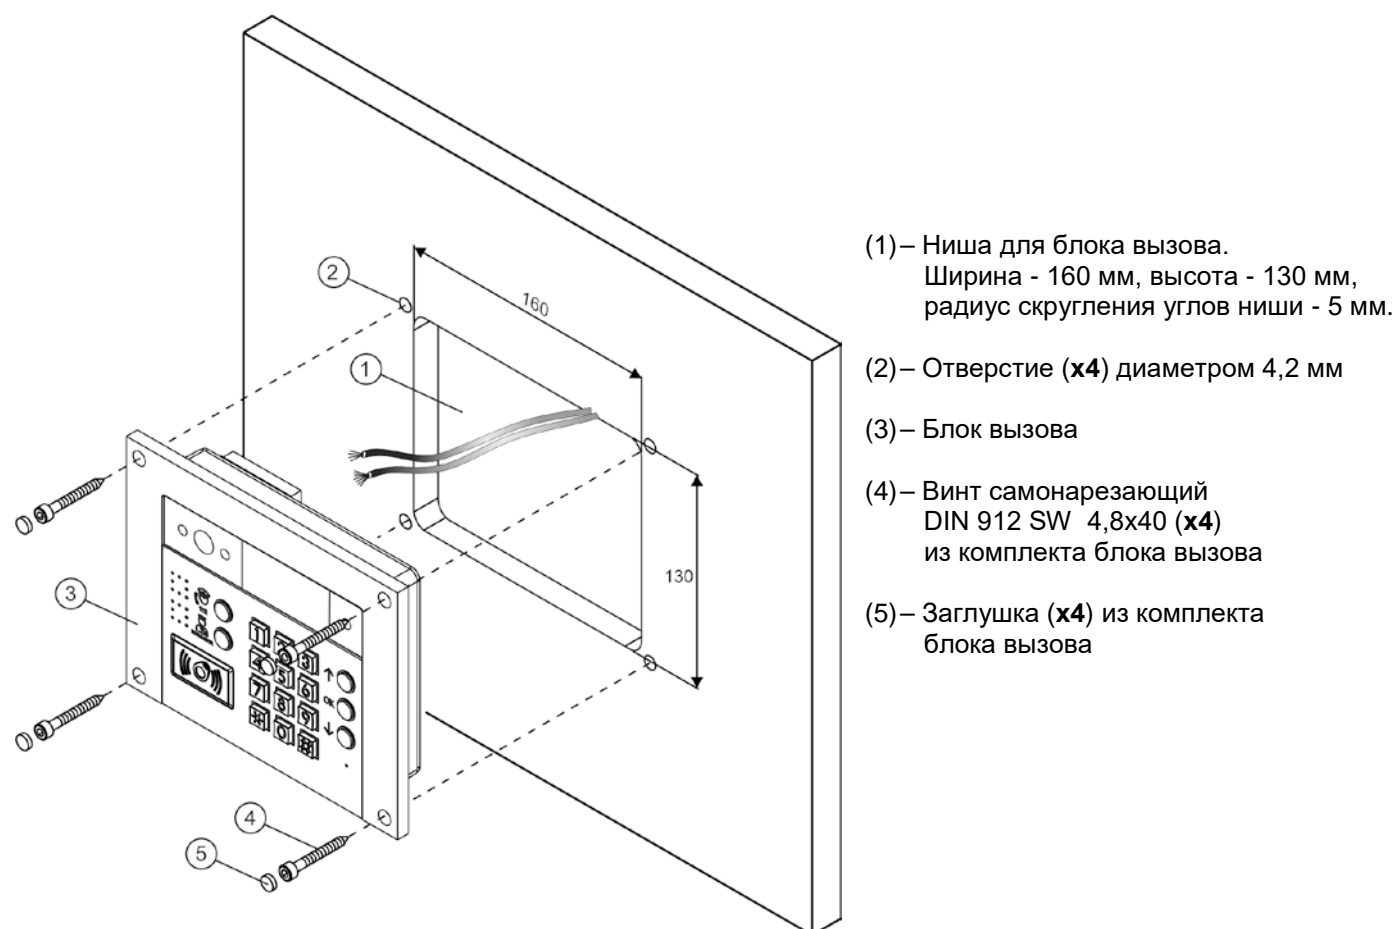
Крепление блока вызова на неподвижную часть металлической двери
